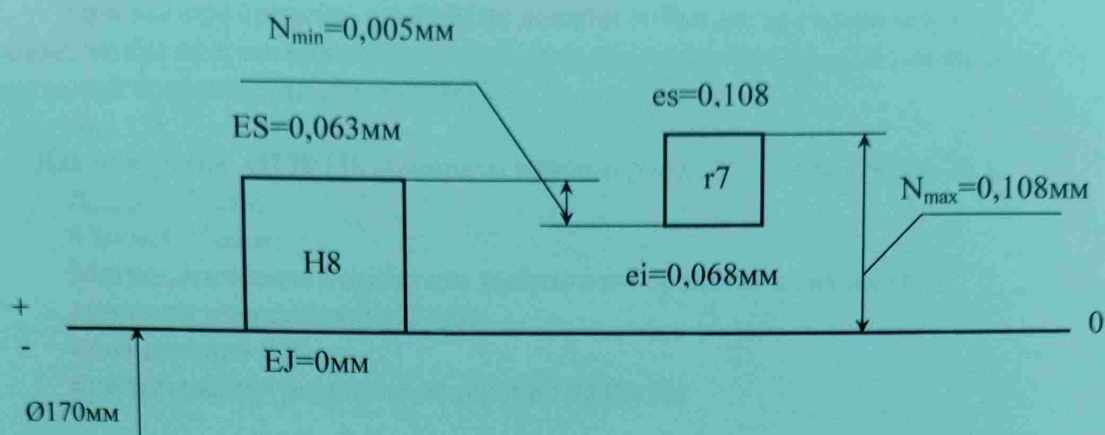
a - Схема расположения полей допусков отверстия и вала.
